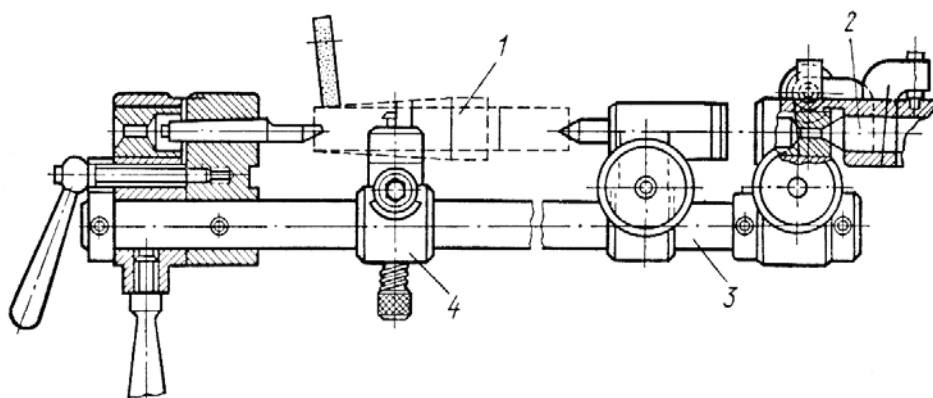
Делительное приспособление для конической заточки задней поверхности режущей части метчика:
